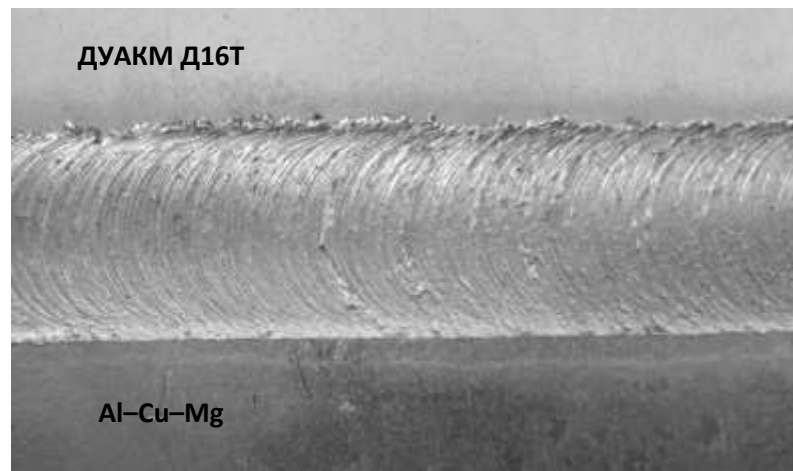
Внешний вид лицевой поверхности сварного соединения алюминиевого сплава системы Al–Cu–Mg с ДУАКМ Д16Т + 20% Al₂O₃
